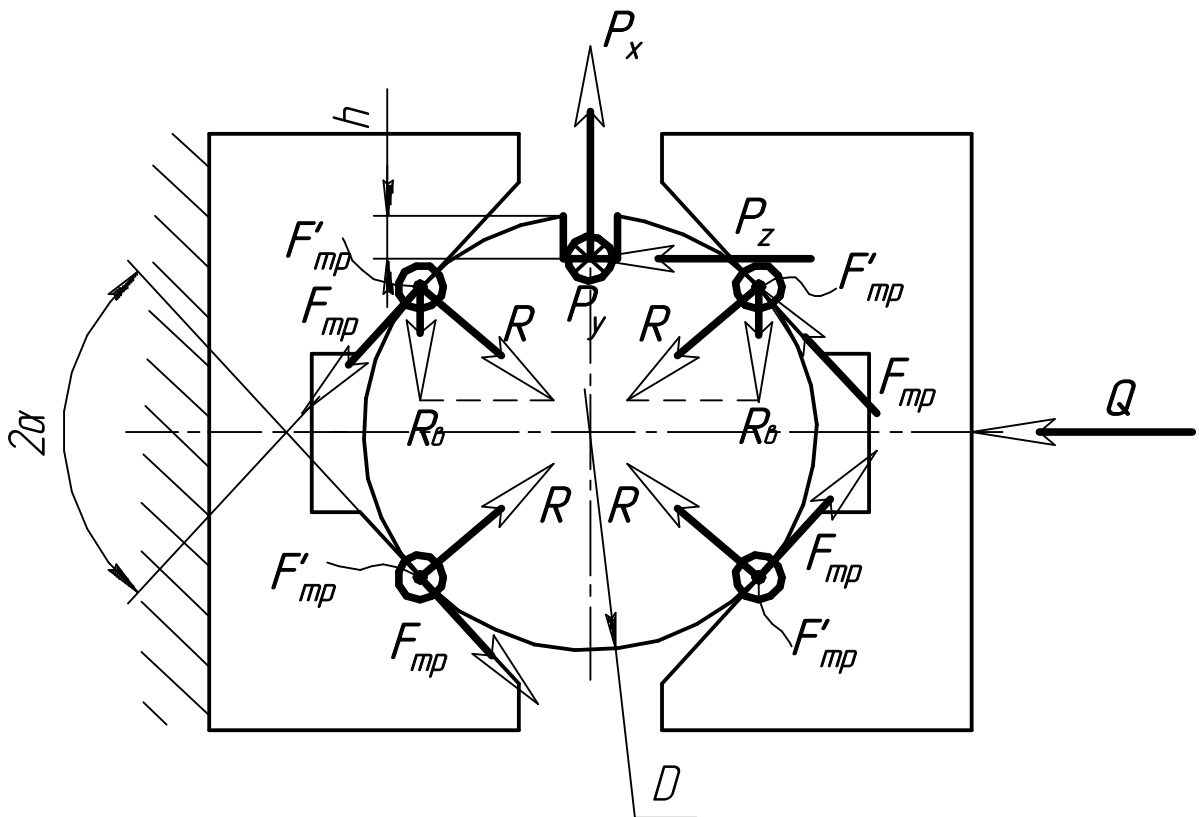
Розрахункова схема для визначення зусилля закріплення деталі при фрезеруванні шпонкового пазу кінцевою фрезою
